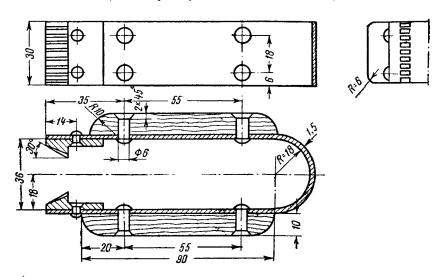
Приспособление для зачистки концов секций (размеры в мм).
